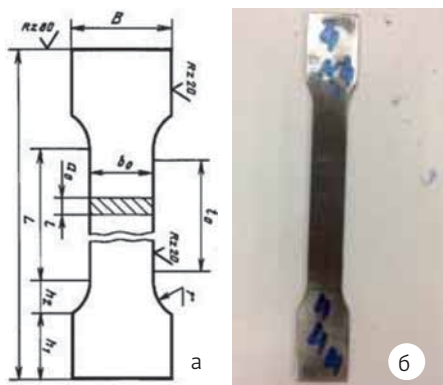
Плоский образец для испытаний на растяжение: а) эскиз образца; б) натуральный образец
